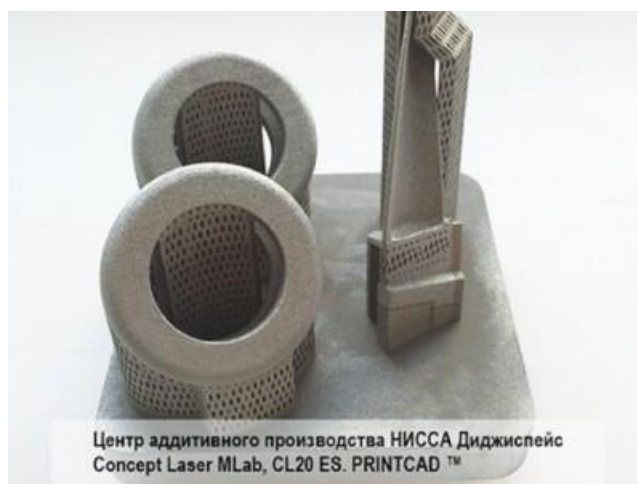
Вариант конструкции поддержек соединительного блока
